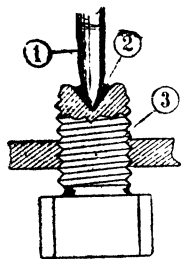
Смазка акса: 1 — акс; 2 — масло в центровом винте; 3 — центральный винт
